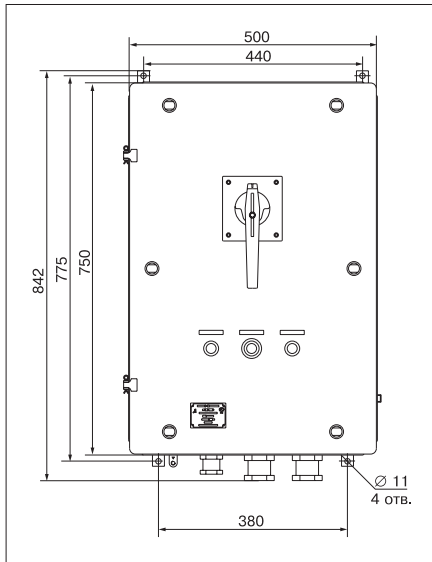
Габаритные и установочные размеры ящика ввода на токи до 80...250 А.
